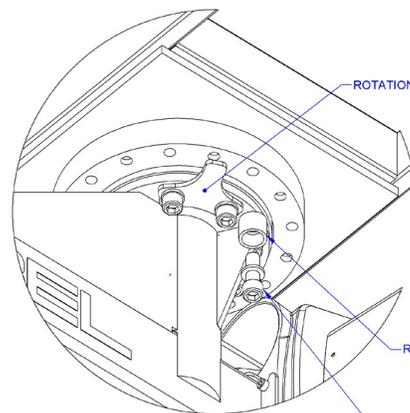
D. Installation des Rotationsanschlags der Hängearm-Baugruppe.
